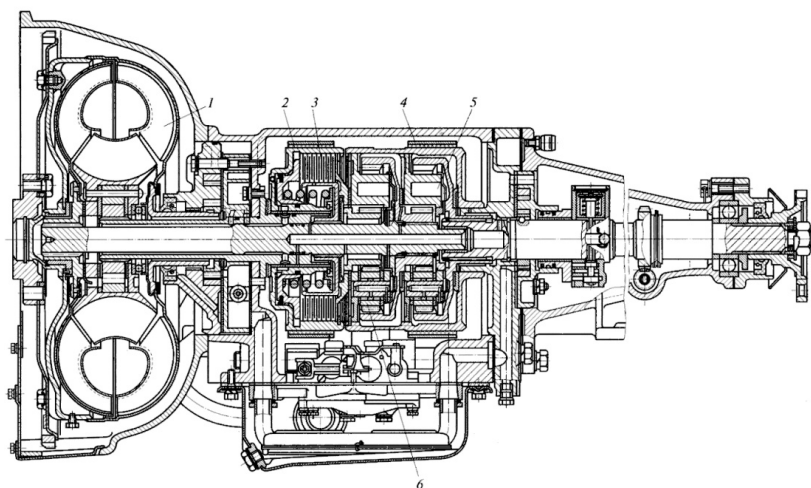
Гидромеханическая коробка передач легкового автомобиля
